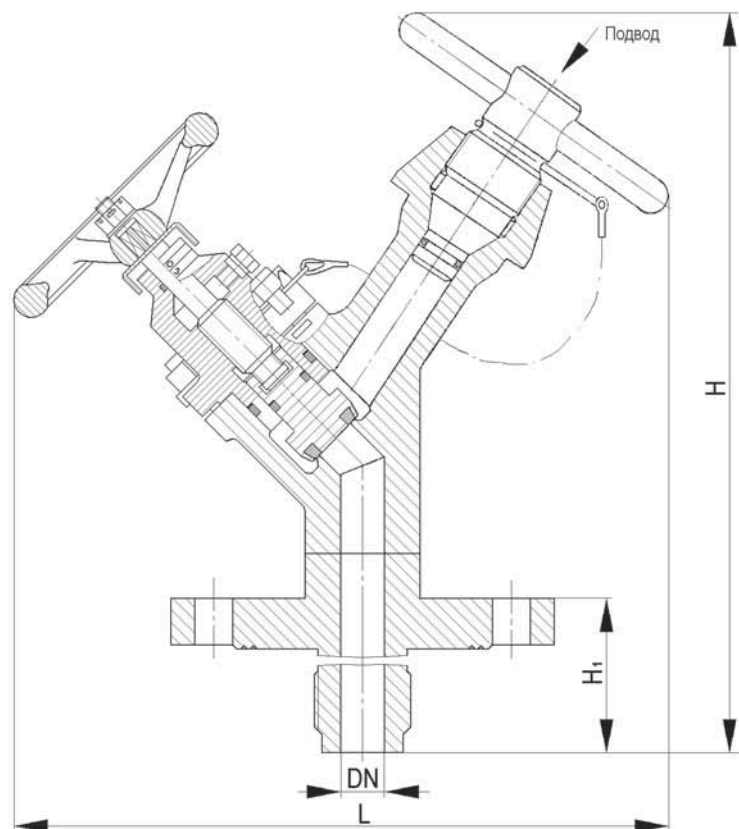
Клапан запорный угловой ручной под безрезьбовой наконечник
